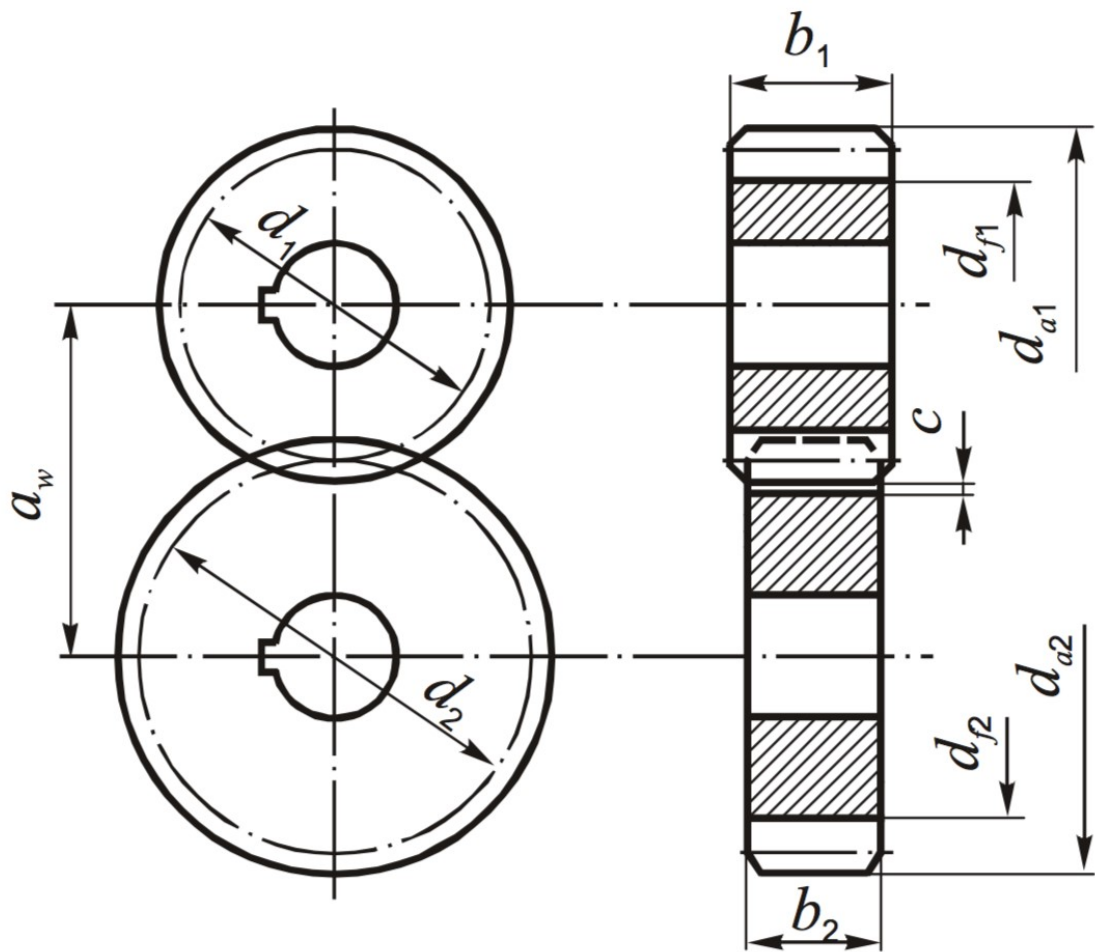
Схема прямозубої циліндричної зубчастої передачі
